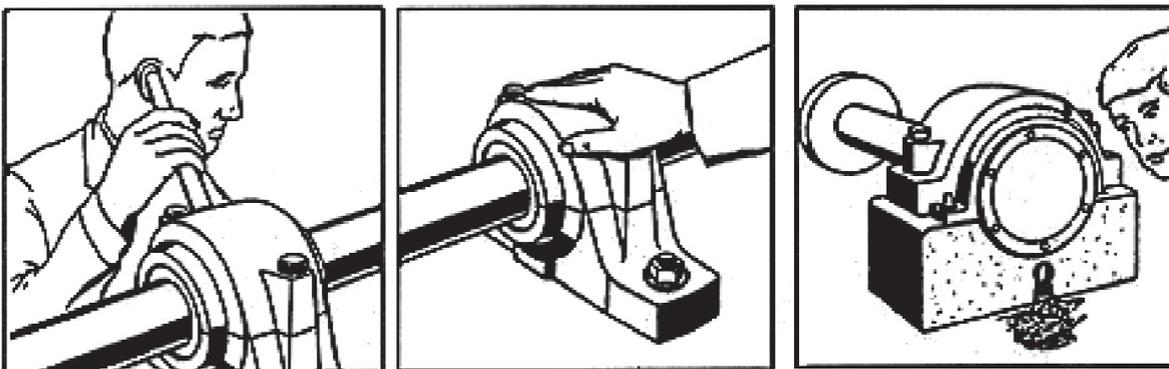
INSPECCIÓN DE RODAMIENTOS O COJINETES
